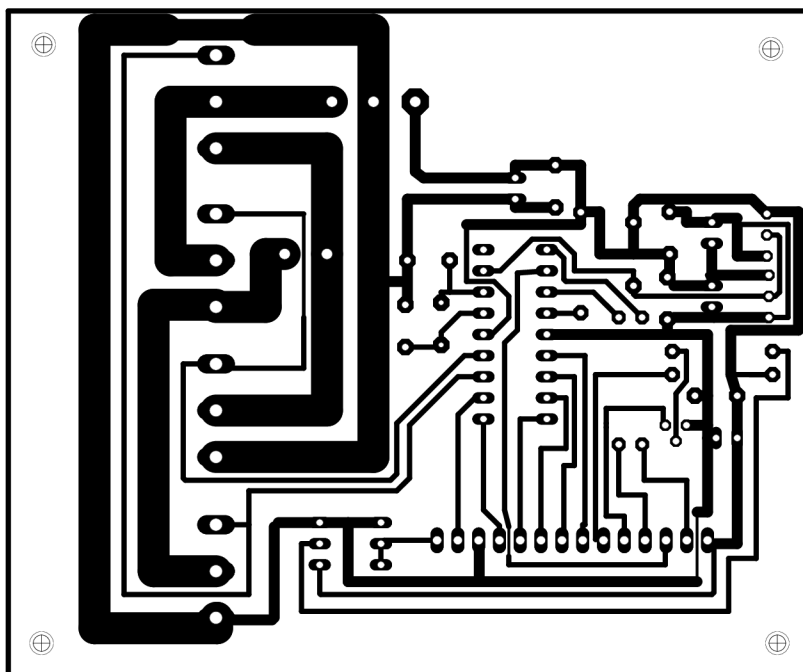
Deska plošných spojů DPS01 - pohled ze strany spojů.
